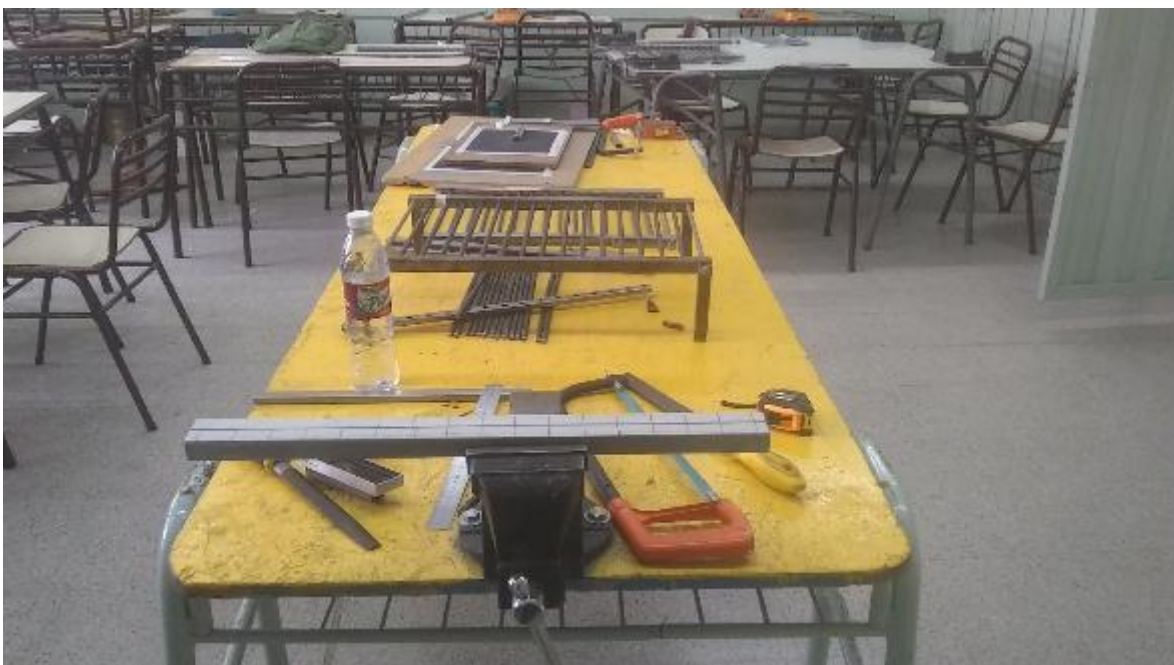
Banco de trabajo adaptado, con herramientas de medida, corte y limado. Donde se realiza trazado y corte de las secciones, de la parrilla.
